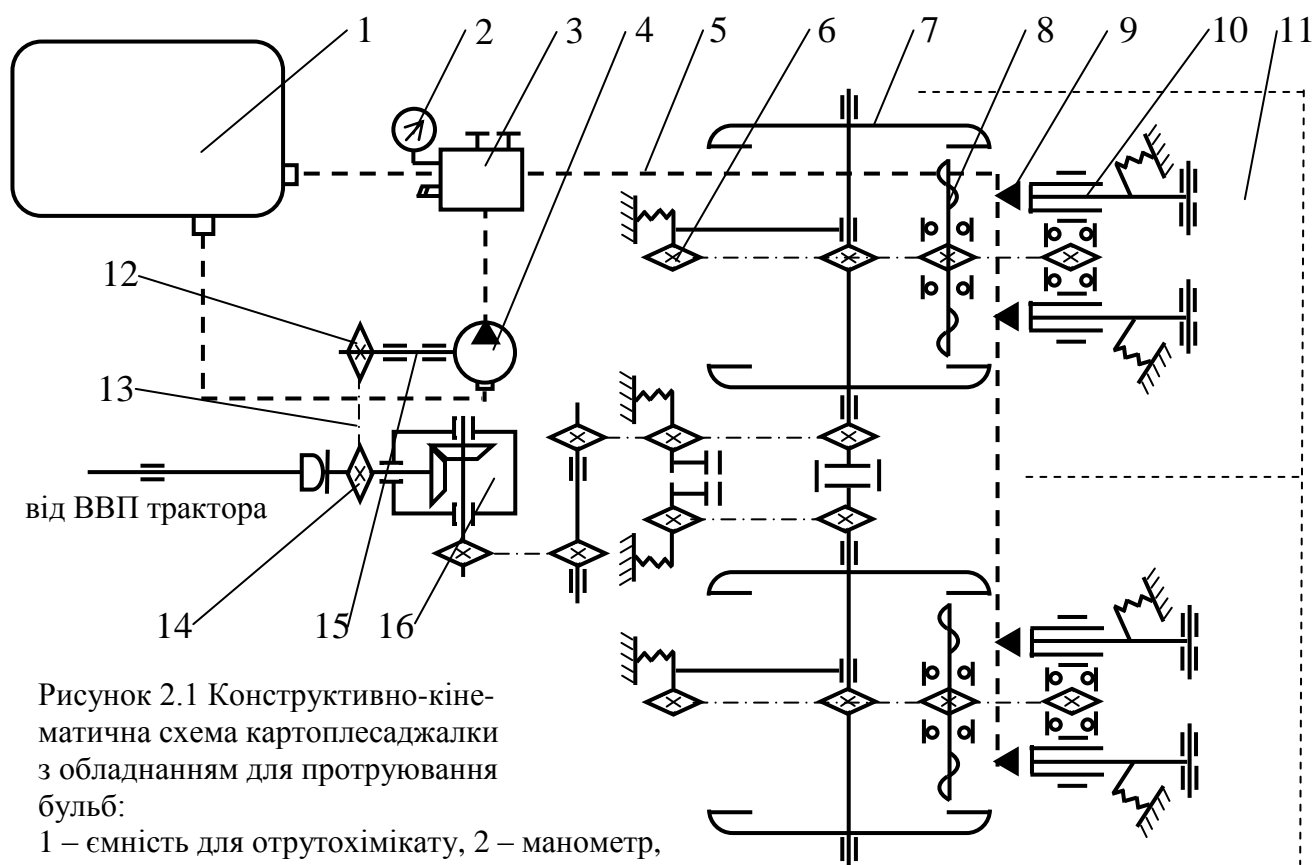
Конструктивно-кінематична схема картоплесаджалки з обладнанням для протруювання бульб:
